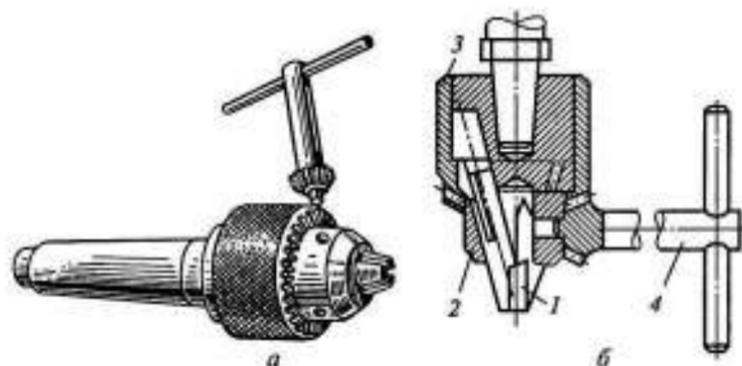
Сверлильный патрон для закрепления сверл с цилиндрическим хвостовиком:
